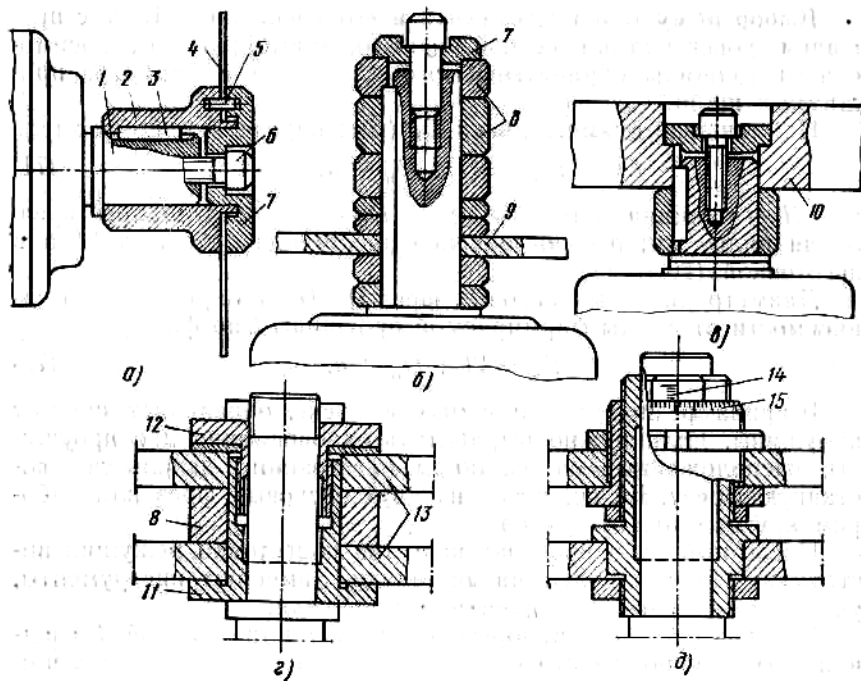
Крепление режущих инструментов в шпинделе рамного шипорезного станка:
